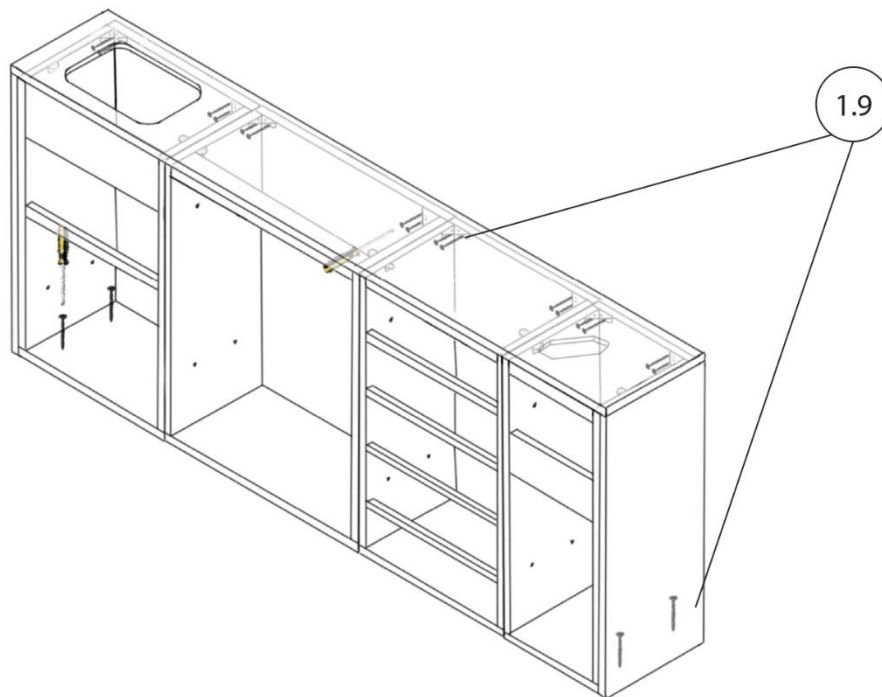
Ensamblaje conjunto 1 a la furgoneta
